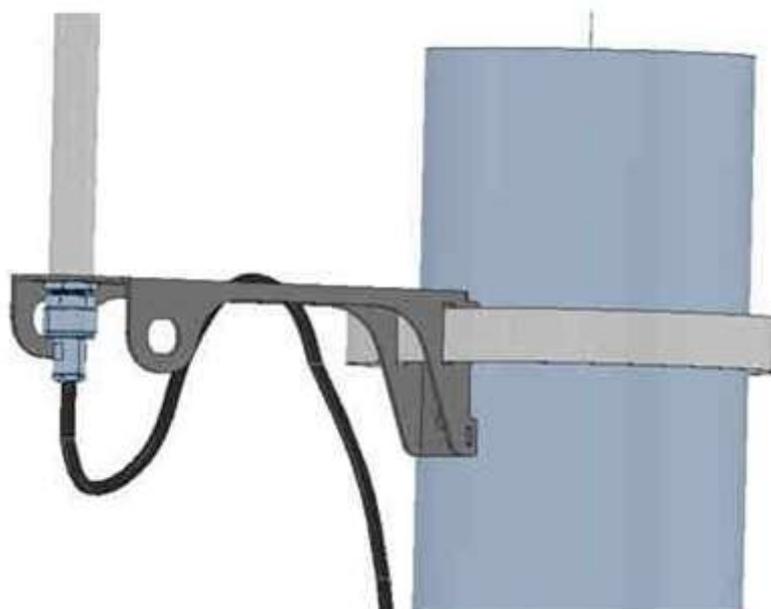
Монтаж на стойку универсальной антенной опоры с помощью строп
